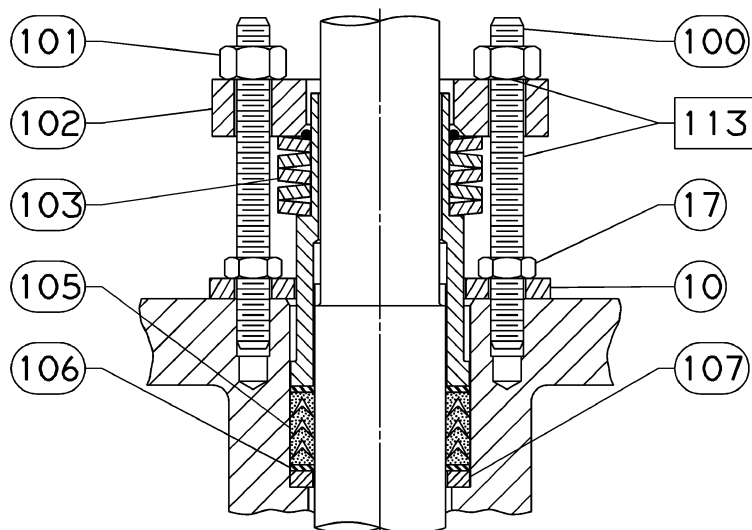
Бесфланцевый корпус клапана модели 8532
